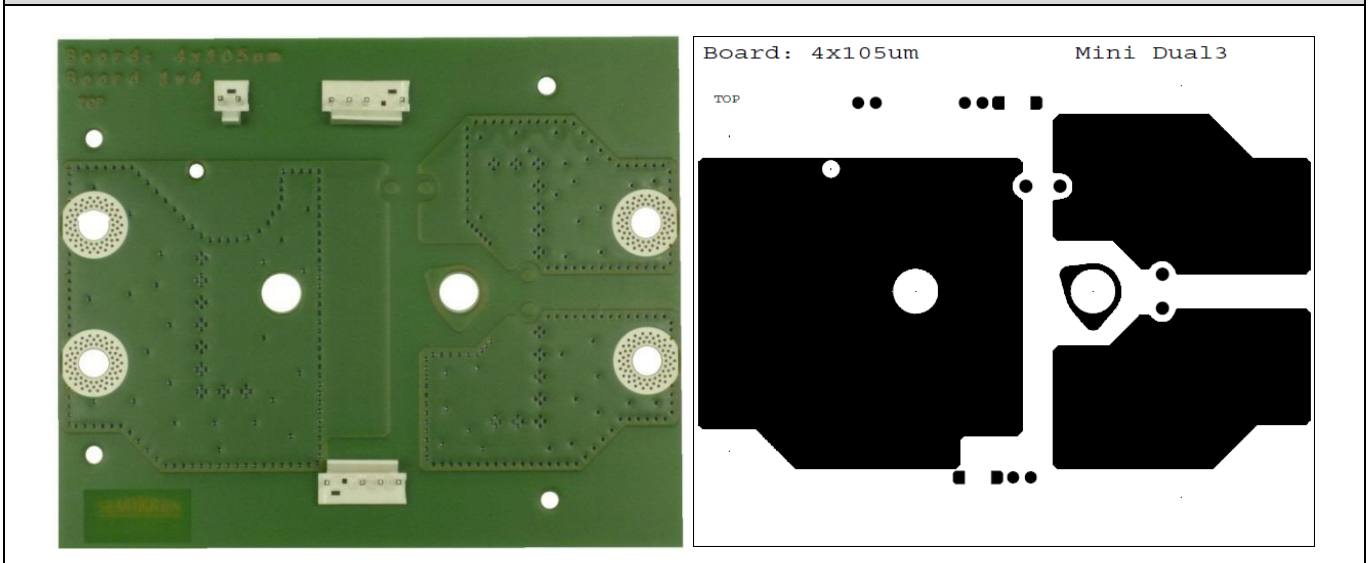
은 MiniSKiiP 모듈 1개용 4-레이어 어댑터 PCB의 실물과 도면입니다. 사진(좌)는 상단 레이어를 사진(우)는 상단 레이어의 PCB 도면입니다.
